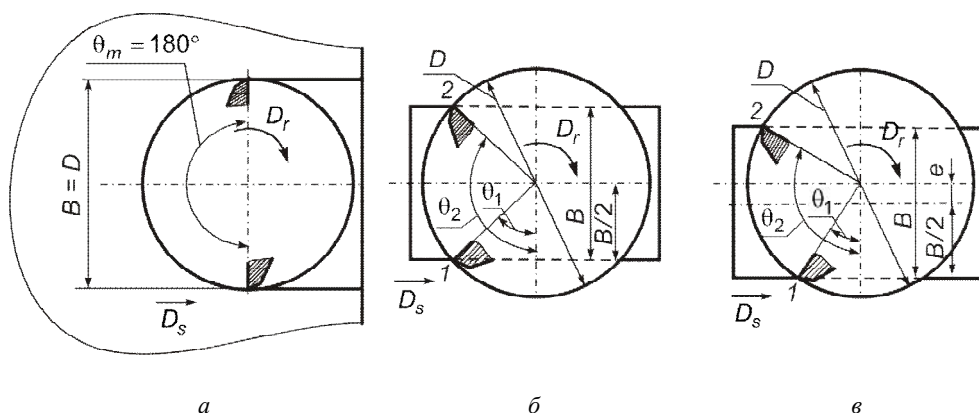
Схемы установки торцевой фрезы относительно заготовки:
